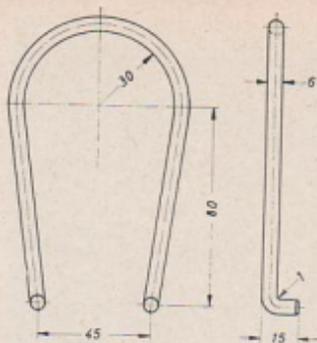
Maßskizze für Ausziehhaken (Selbstanfertigung)
